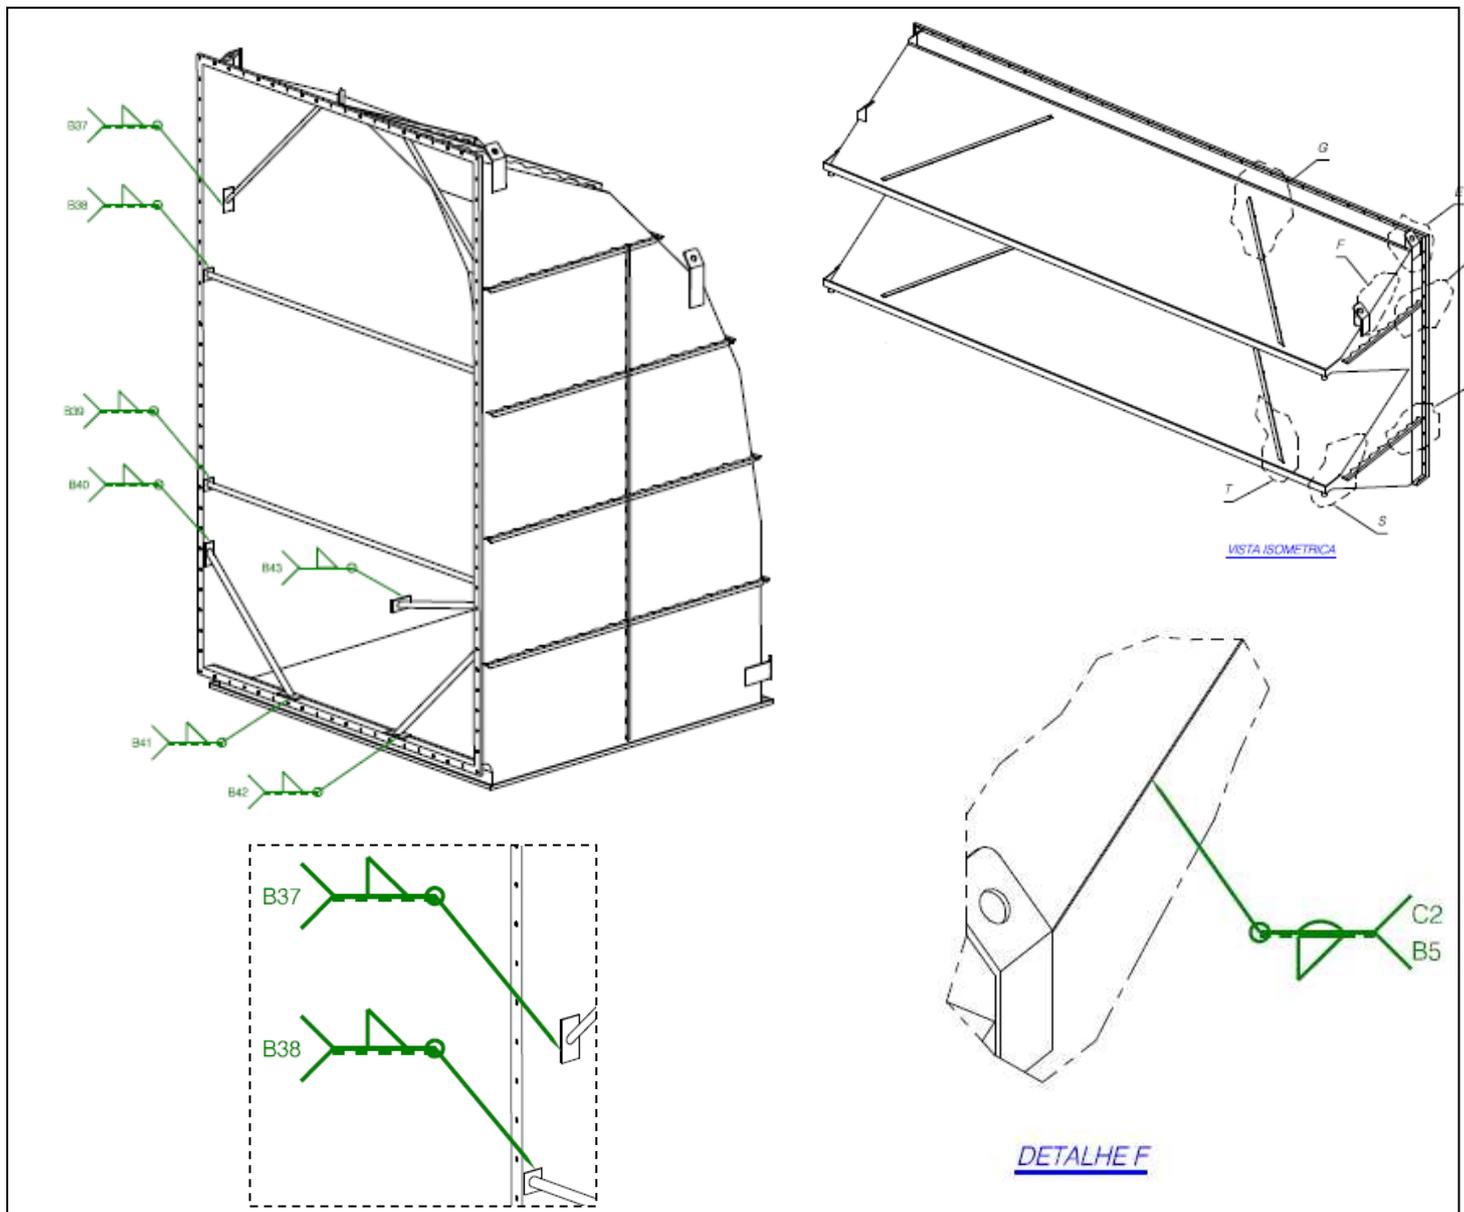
Partes dos desenhos de fabricação com as indicações de solda.
